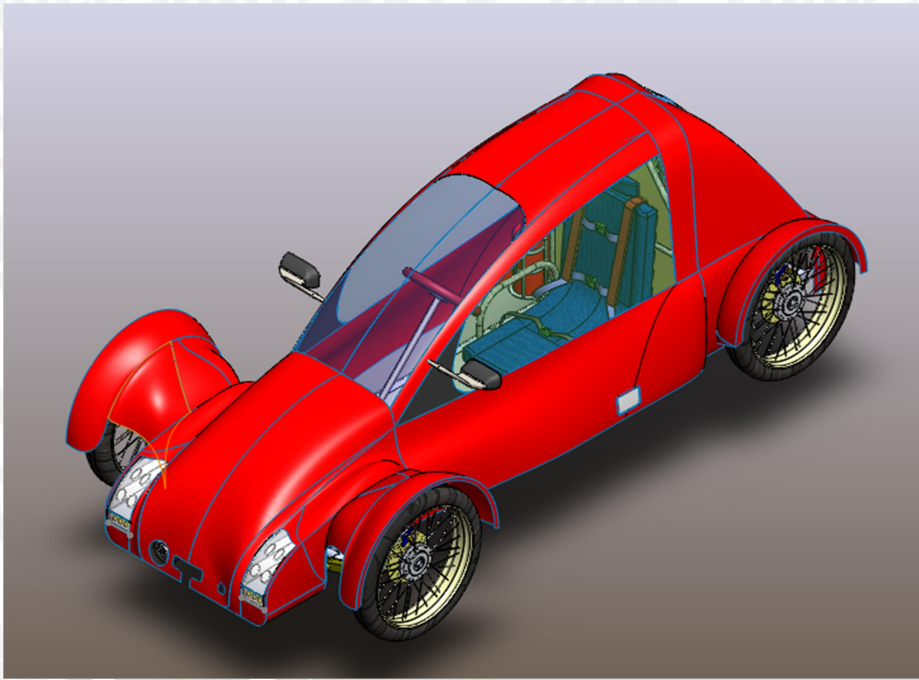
Chasis Marsela Apatte62 tampak samping
